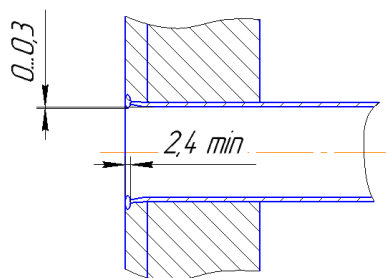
Требования к геометрии сварного шва при сварке труб с трубной доской.
